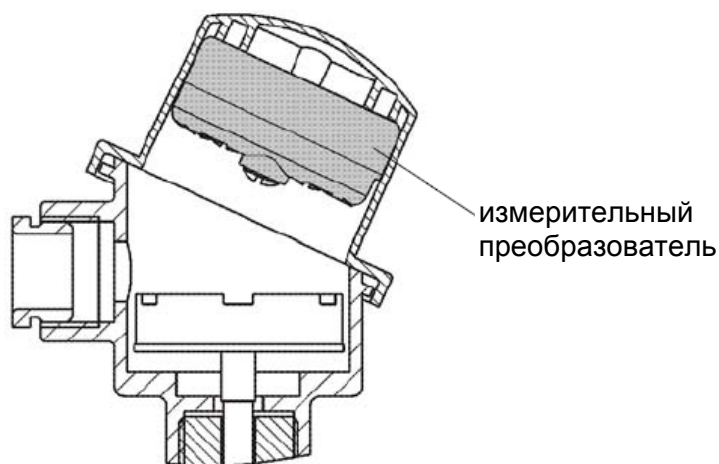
Крепление преобразователя в откидывающейся крышке соединительной головки
